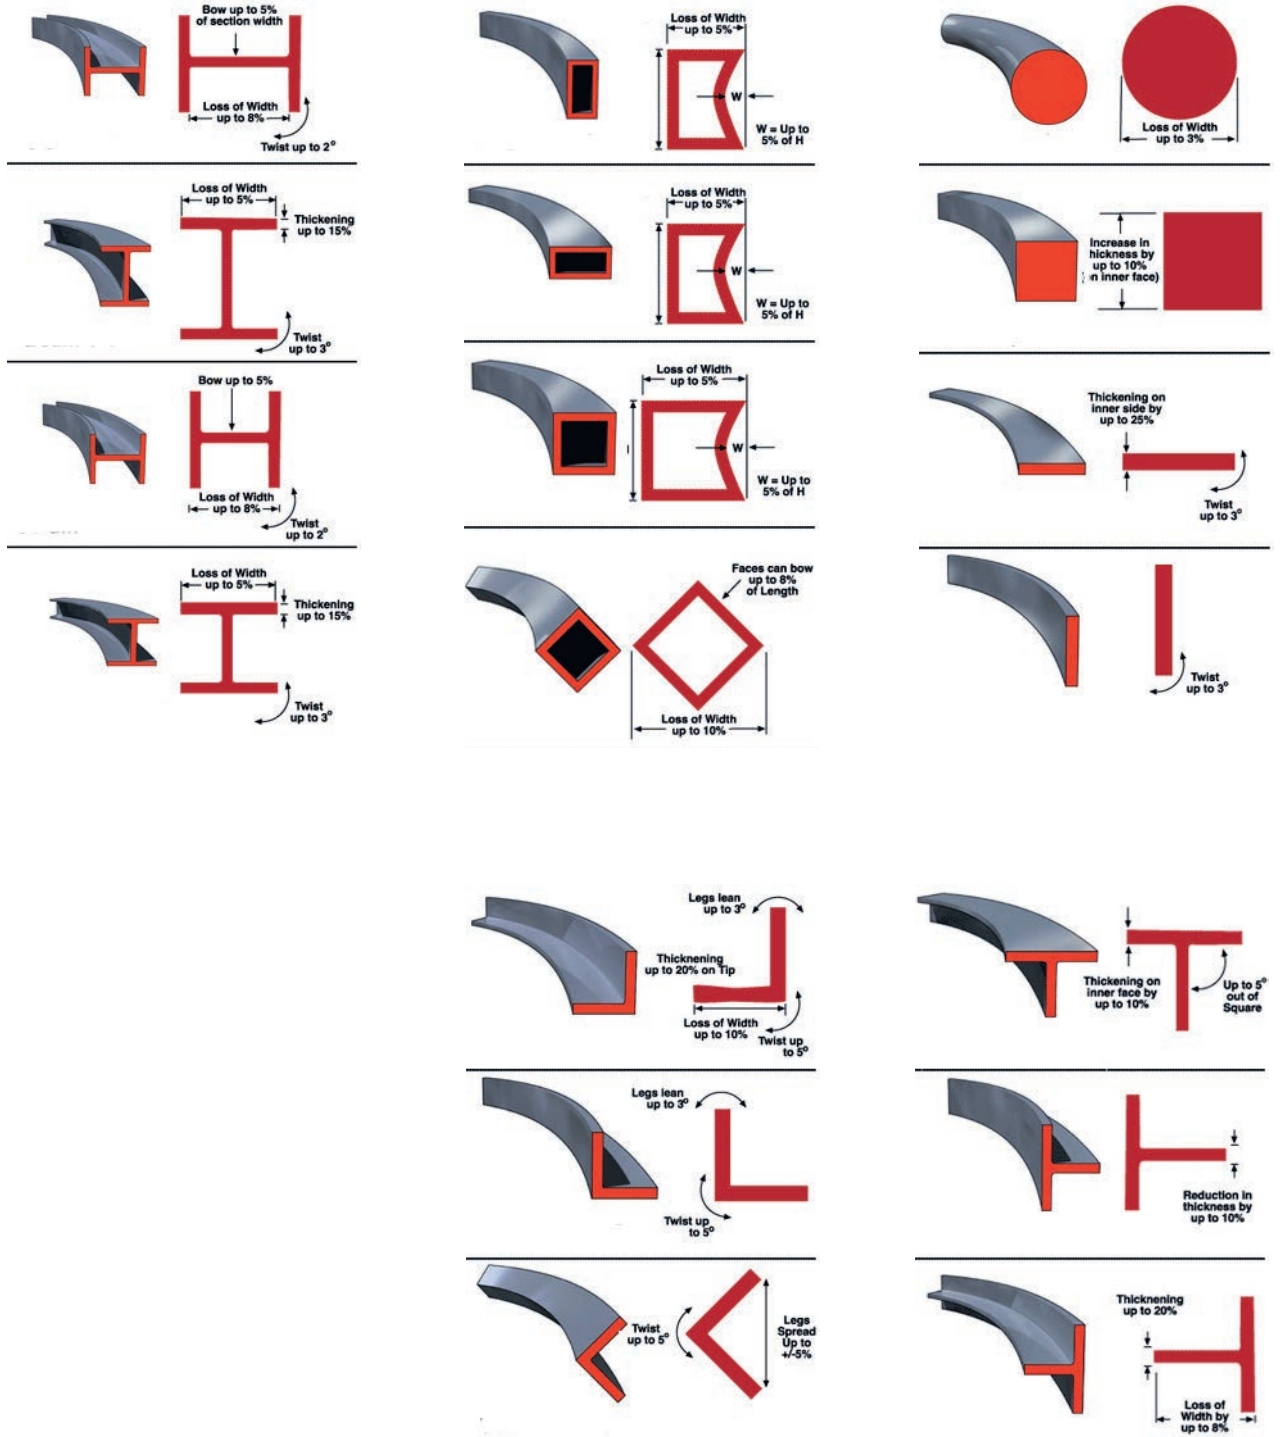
Toepassingsvoorbeelden voor buigwalsen
